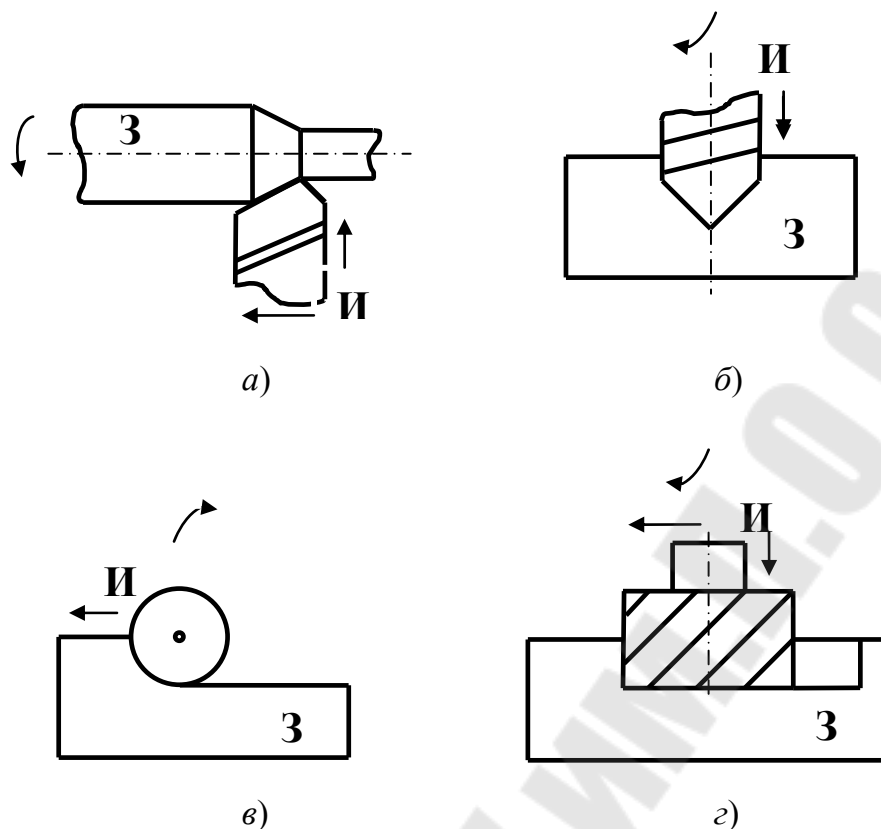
Схемы основных видов механической обработки металлов:
